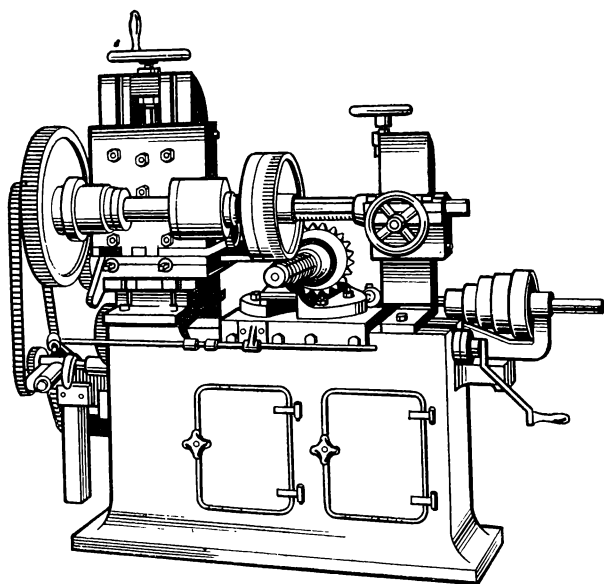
Зубофрезерный станок (конструкции Пфау-тера) для нарезания косозубых цилиндрических колес
